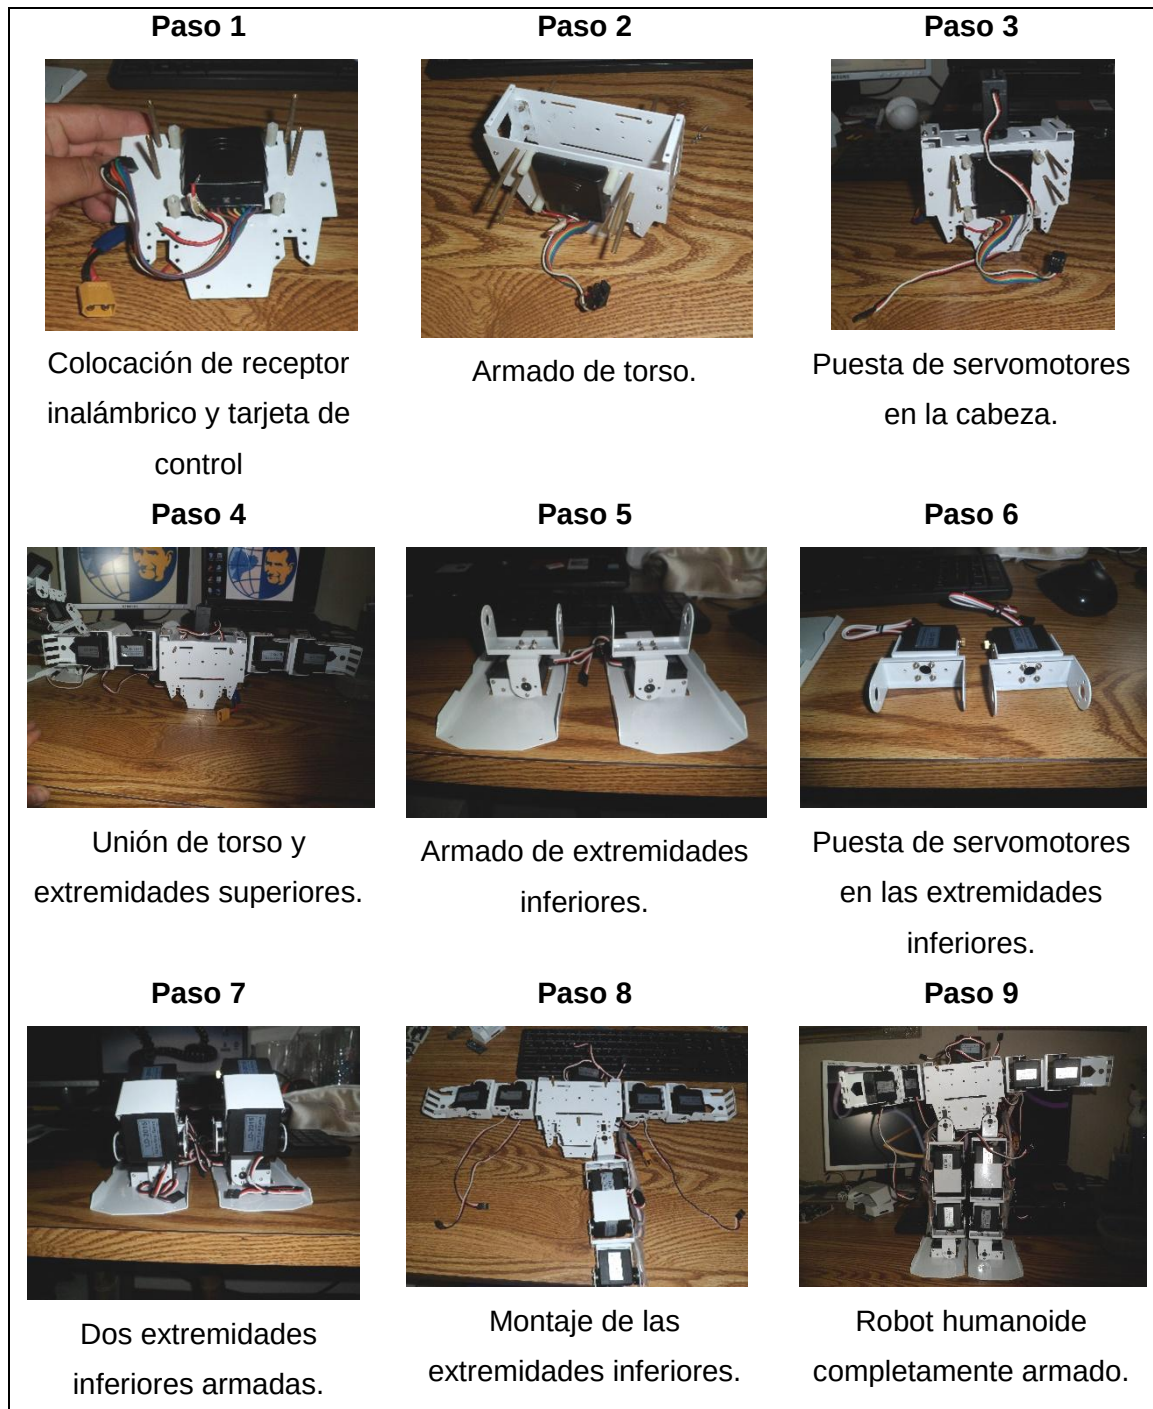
Ensamblaje mecánico de Robo Soul H3.0.
